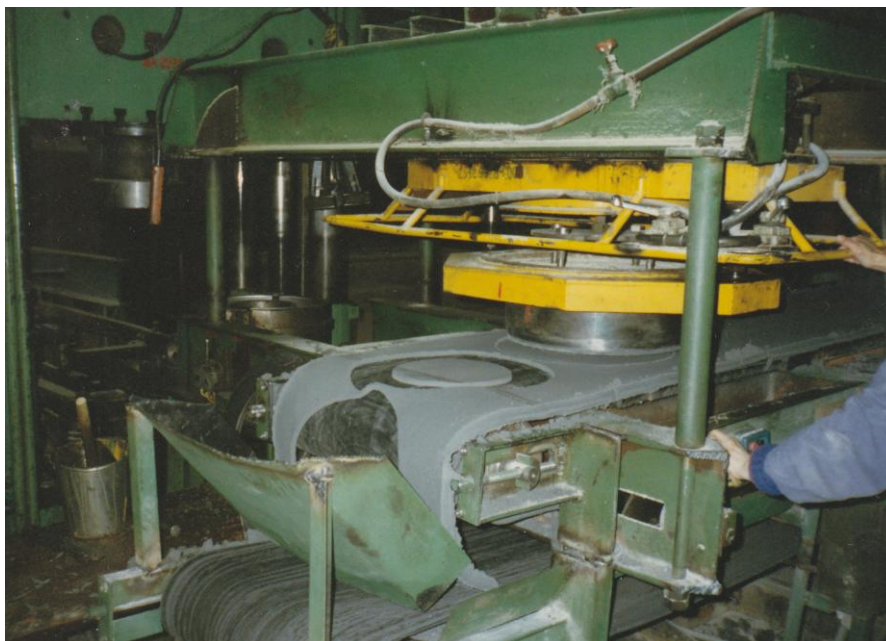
Высечка кольцевых заготовок ножевым штампом
